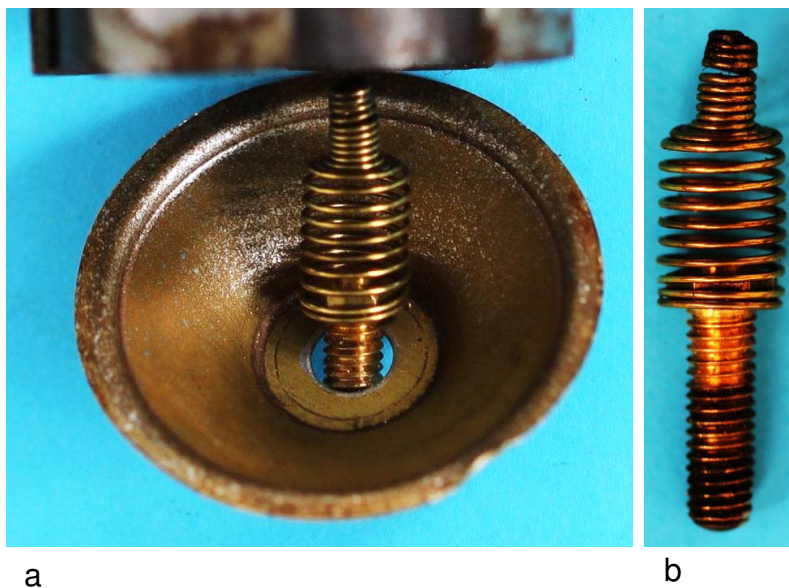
Kabelanschlussbolzen mit eingezogener Schraubenfeder als Schleifkontakt
